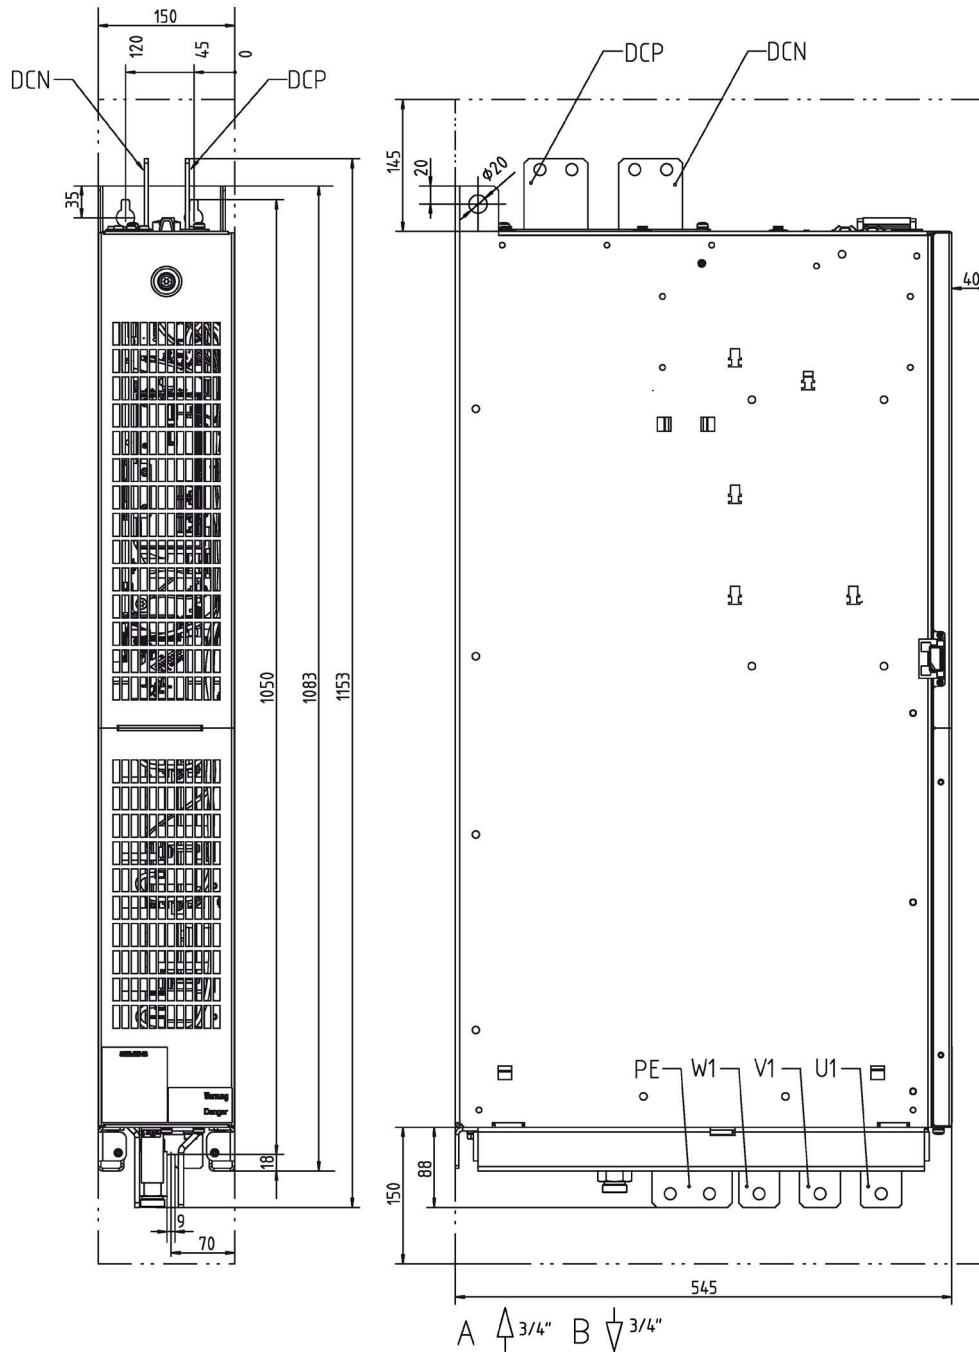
Габаритный чертёж активного модуля питания, типоразмер GXL. Вид спереди, вид сбоку
